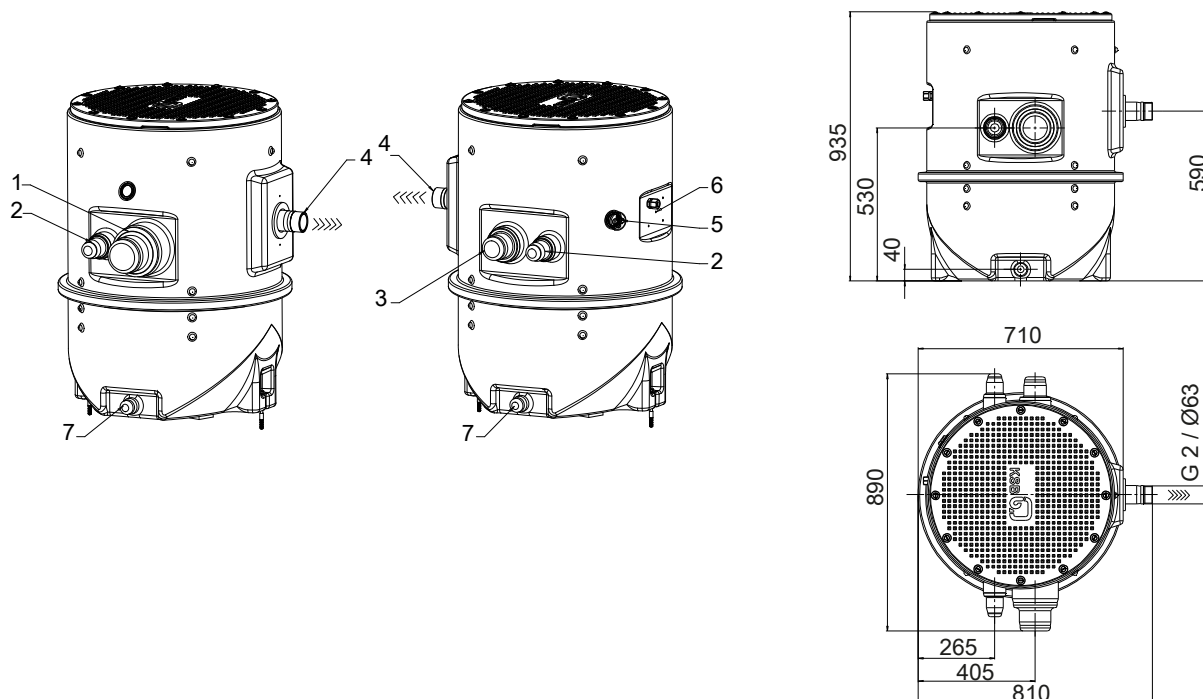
Anschlüsse und Abmessungen Doppelanlage
